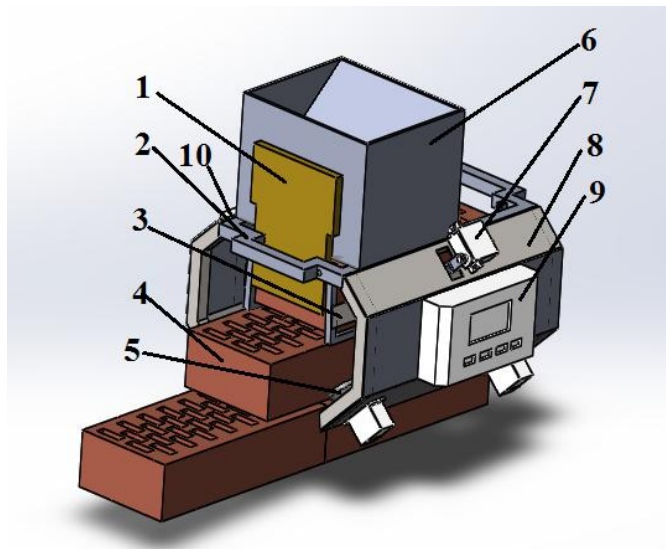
Внешний вид установки для укладки облицовочного кирпича
